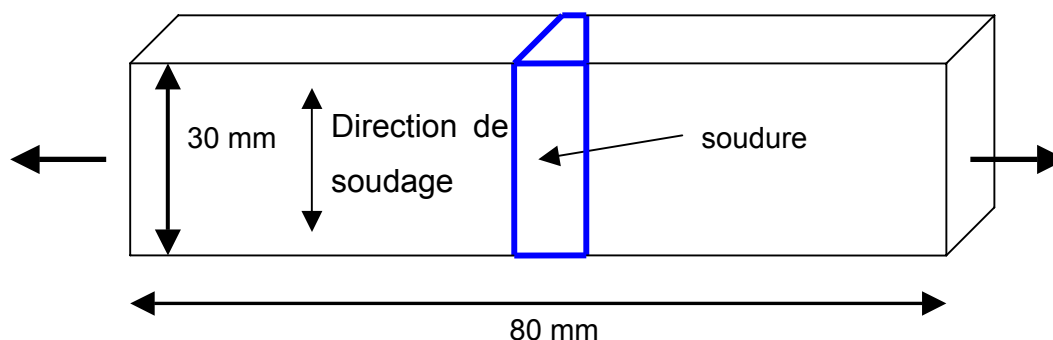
Schéma des éprouvettes de traction avec soudure
